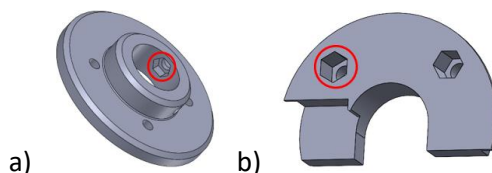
a) Inserto para fixar os adaptadores no veio; b) Inserto para fixar os componentes.
